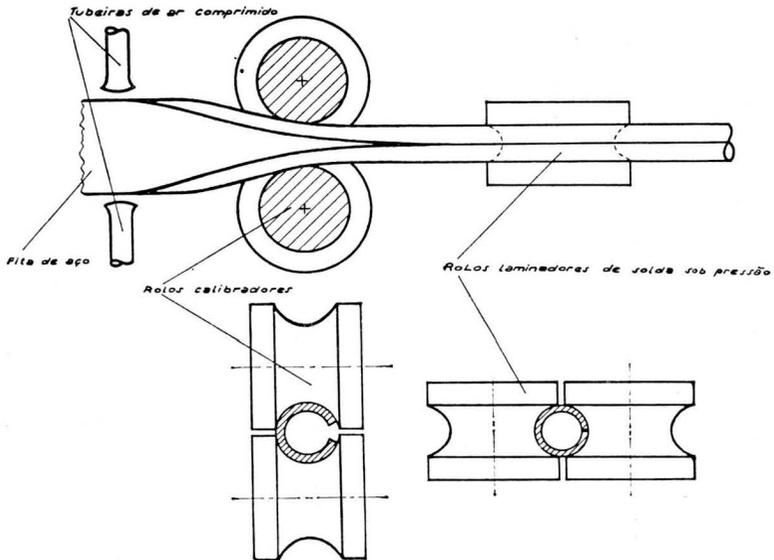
Fabricação de tubos pelo processo Fretz-Monn, de produção contínua.
